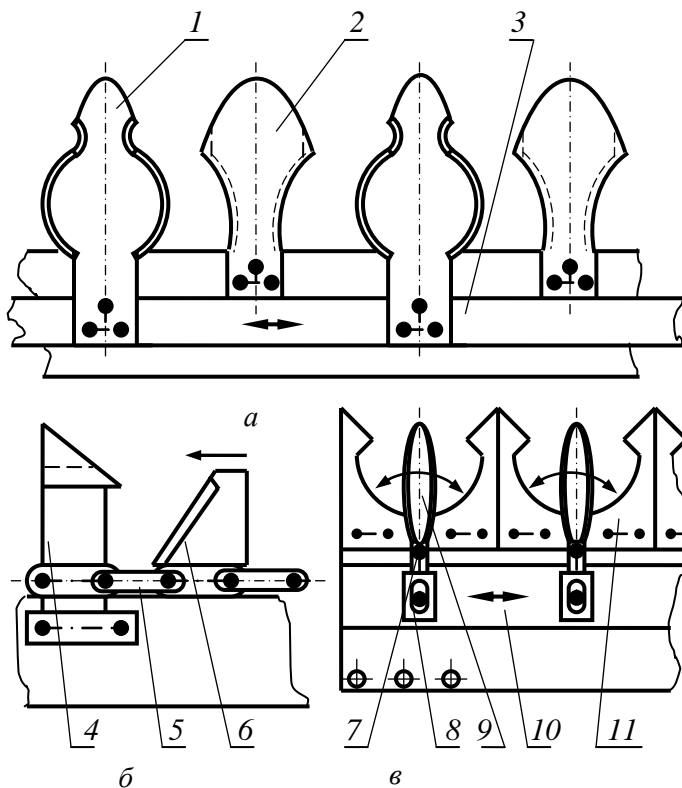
Схемы рабочих органов косилок для срезания грубой растительности: а – с возвратно-поступательным движением ножей; б – цепной с поступательным движением ножей; в – с колебательным движением ножей.
